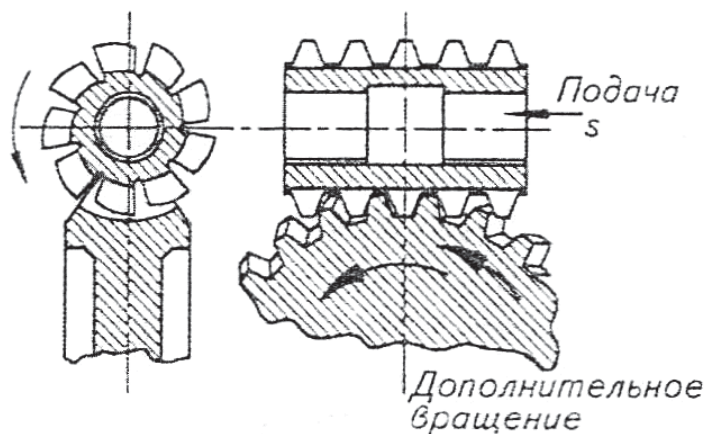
Схема нарезания зубьев червячного колеса червячной фрезой с тангенциальной подачей
